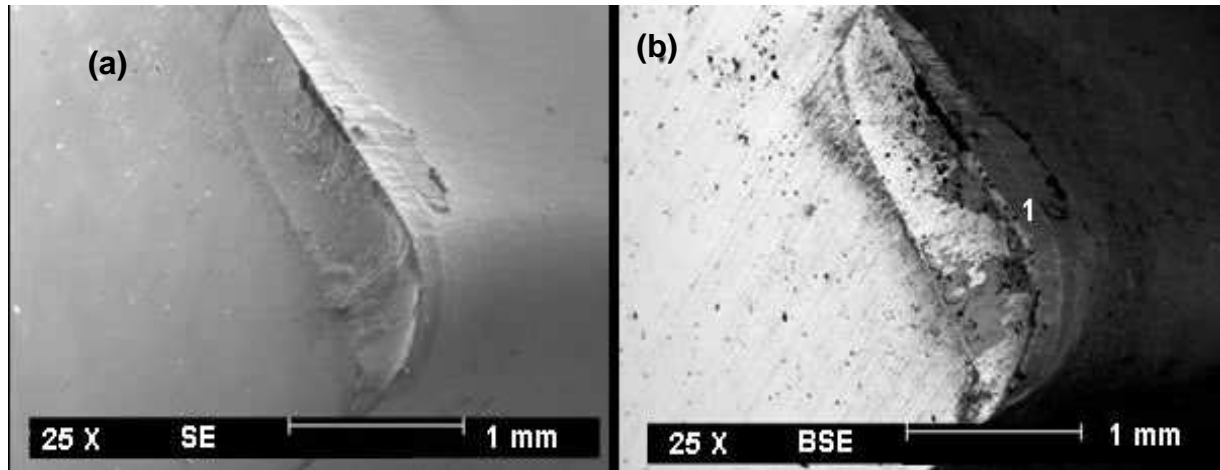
Textura (a) e imagem de composição (b) das superfícies da ferramenta de corte usada na usinagem do ferro fundido cinzento FC 25 com 0,18% S a $v_c = 150$ m/min.
